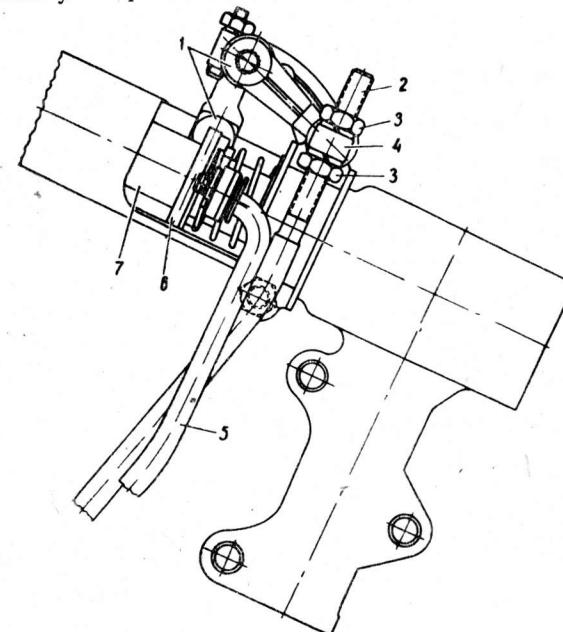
Регулировочный узел механизма управления коробкой передач:
